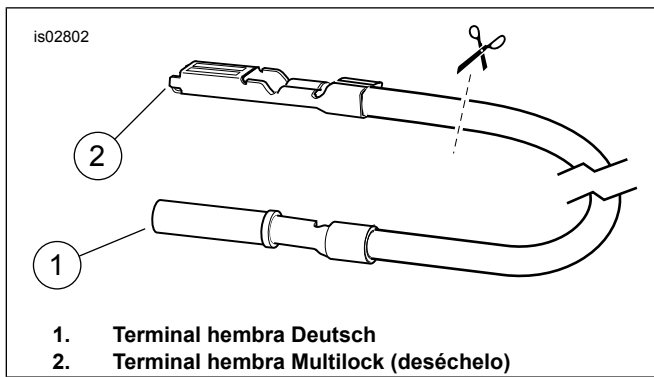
Corte del terminal Multilock del cable conductor del adaptador
